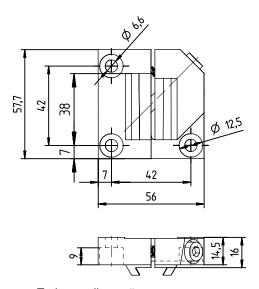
Desenho dimensional BPS com tampa de conexão MK 358
